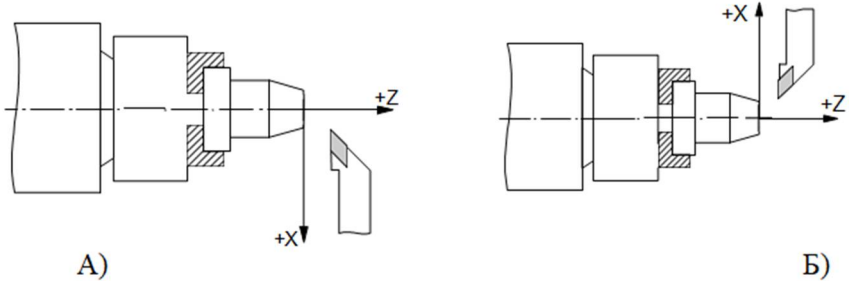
Система координат заготовки при токарній обробці, в якій інструмент направлений до осі обертання від передньої площини верстата (А), і в якій інструмент направлений до осі обертання у бік передньої площини верстата (Б).
